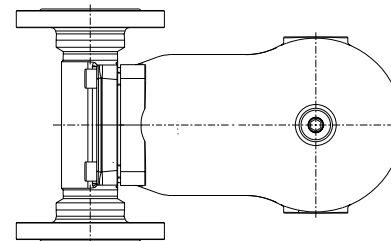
1 mit Flanschen - horizontale Einbaulage
